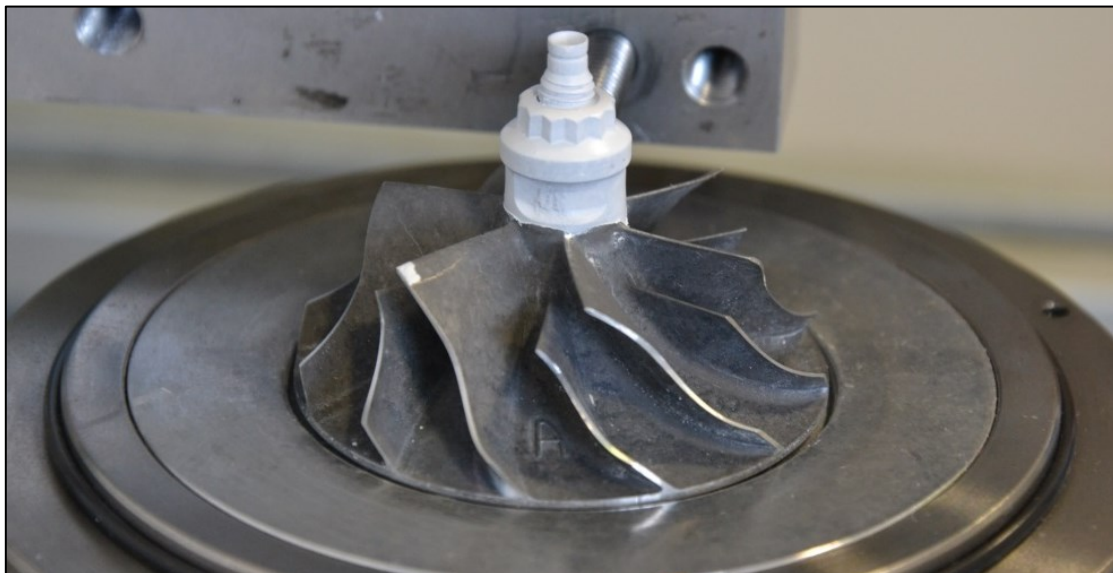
Rueda del compresor con una muesca de equilibrado pintada de blanco
